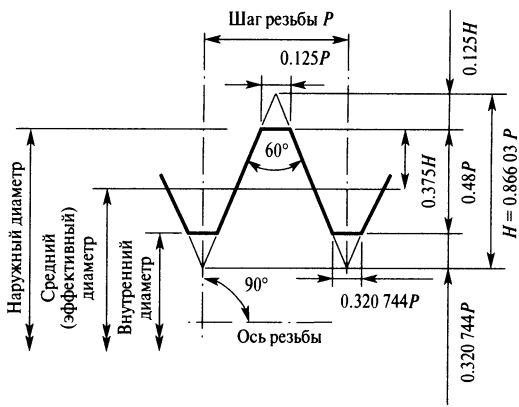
Форма миниатюрной метрической резьбы, по ISO
